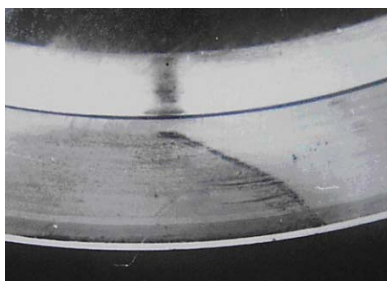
Вид поверхностей контакта (цилиндрической и конической) при формовке швеллера из алюминиевой полосы толщиной 1,0 мм, окрашенной тёмной нитрокраской, в валках из прозрачного материала
